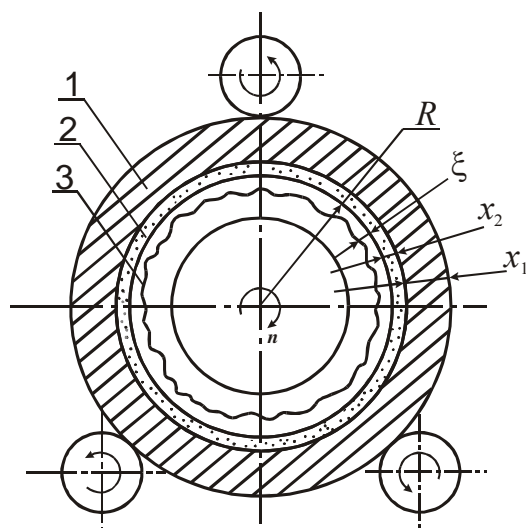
Термодинамическая схема центробежной отливки втулок цилиндров с применением принудительного охлаждения внутренней поверхности
